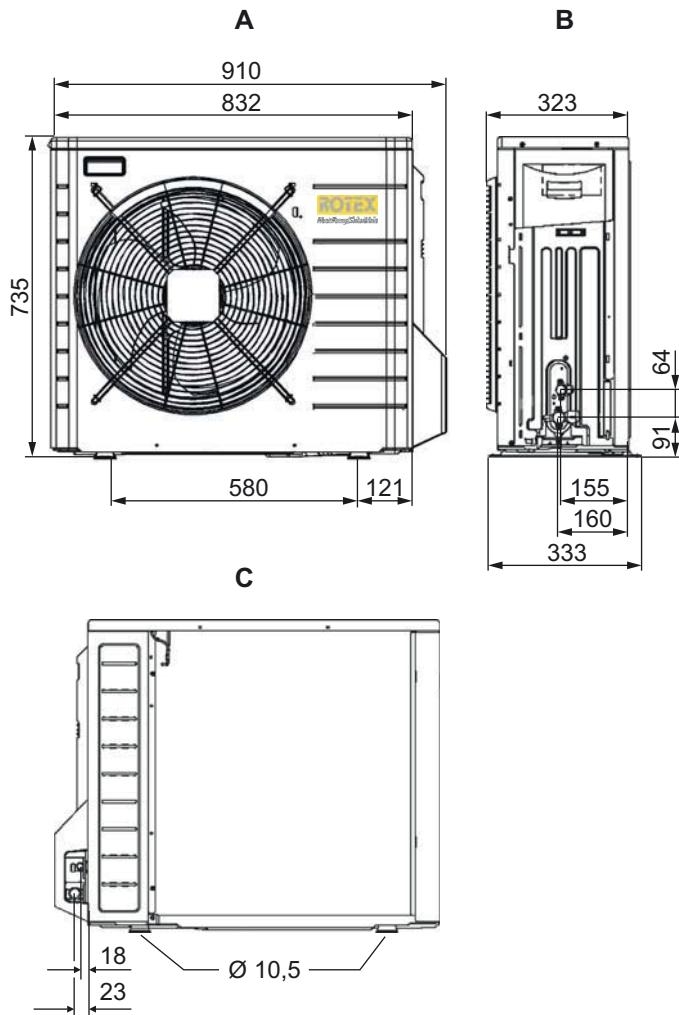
Abmessungen Außengerät RRLQ 4-8 kW
